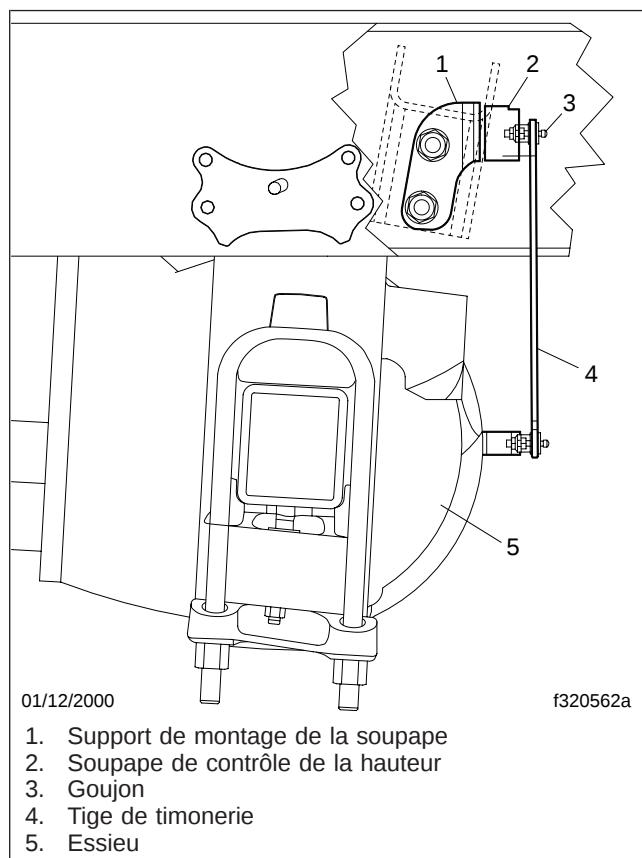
, Installation typique de la soupape de contrôle de la hauteur Barksdale (vue de profil)
